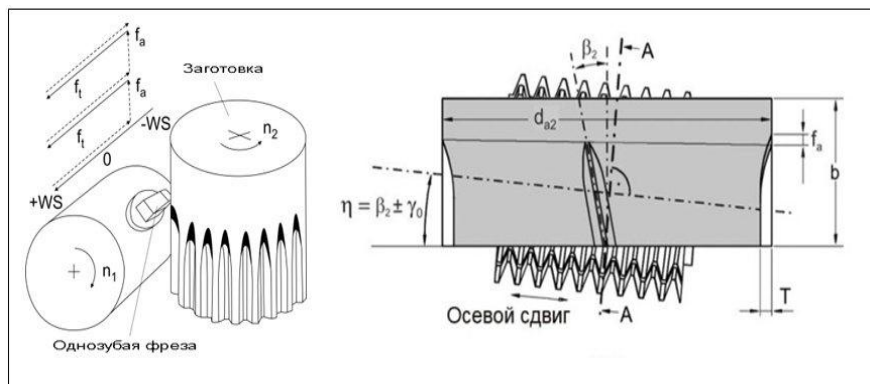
Схема перемещений и геометрические параметры червячной фрезы
